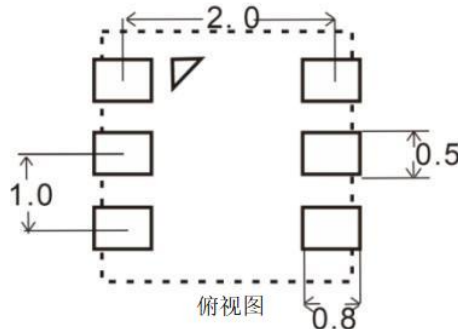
推荐传感器 PCB设计尺寸（单位：mm），外围虚线部分为SMD封装外部尺寸
